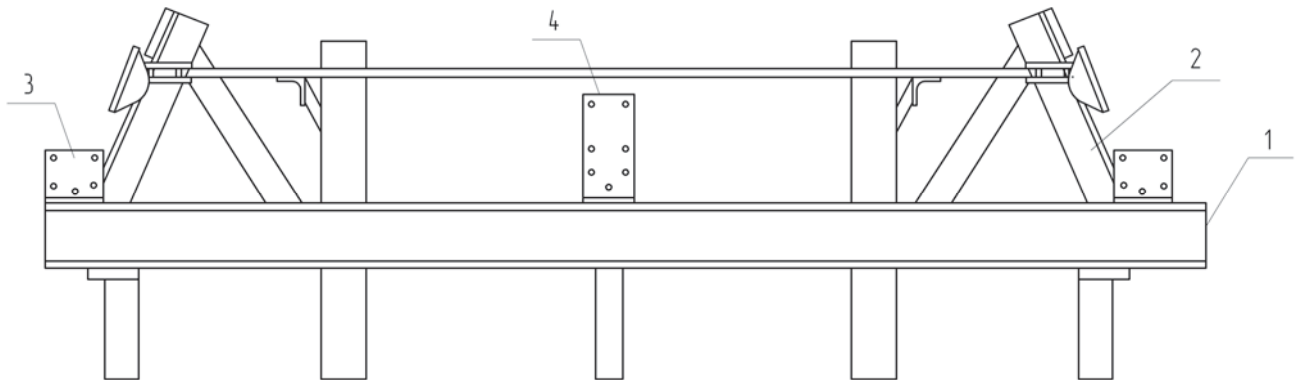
Экспериментальная установка для изготовления и подбора конструктивных размеров ходовой тележки
